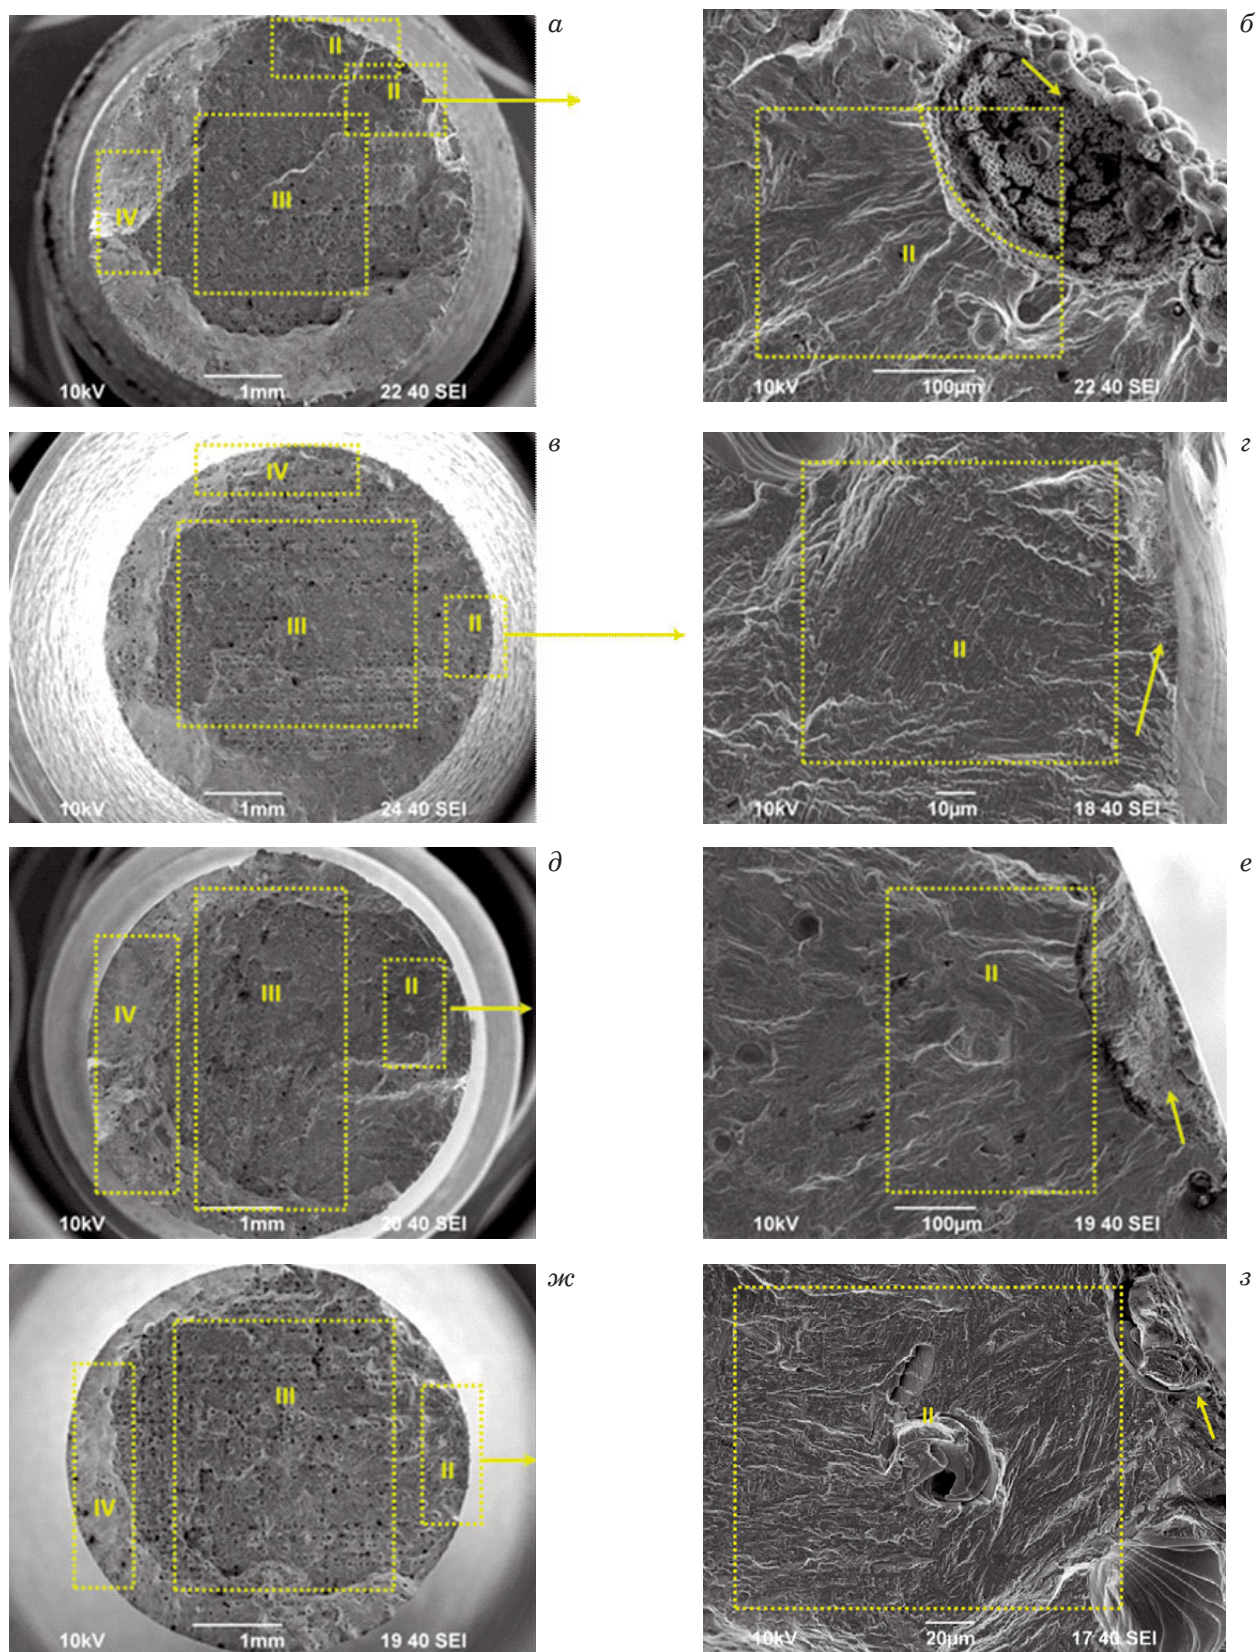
Типичные изображения изломов ПЛС-образцов Ti – 6Al – 4V без обработки (*a, б*) и после различных видов обработки поверхности: виброгалтовочной (*в, з*); токарной (*д, е*); гидроабразивной (*ж, з*); римскими цифрами обозначены различные зоны разрушения: зарождения микротрещины (I), медленного роста трещины (II), быстрого роста трещины (III) и долома (IV)
